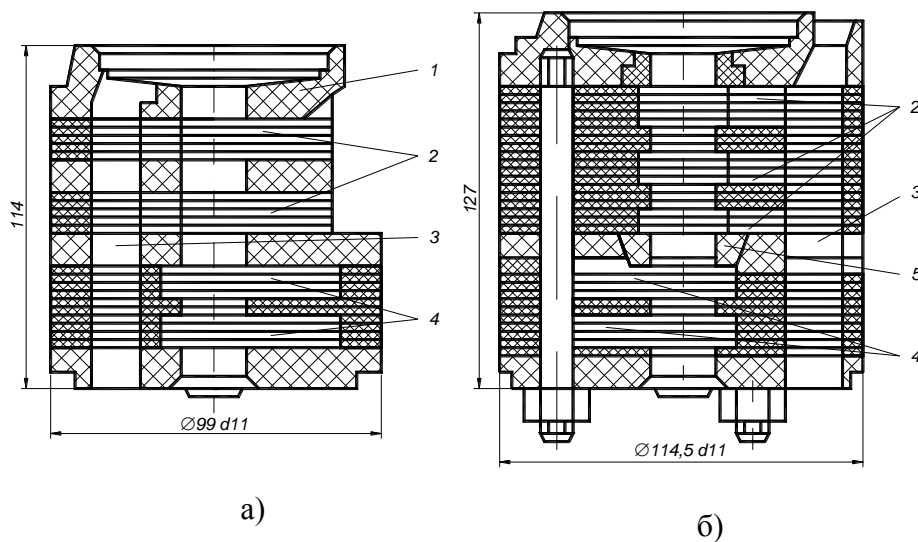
Камера дугогасительная выключателя ВК (ВКЭ-М-10): а) – номинальный ток 630 и 100 А; б) – номинальный ток 1600, 2000 и 3150; 1 – кольцо; 2 – щели дутьевые; 3 – канал вертикальный; 4 – карманы; 5 – втулка конусная
